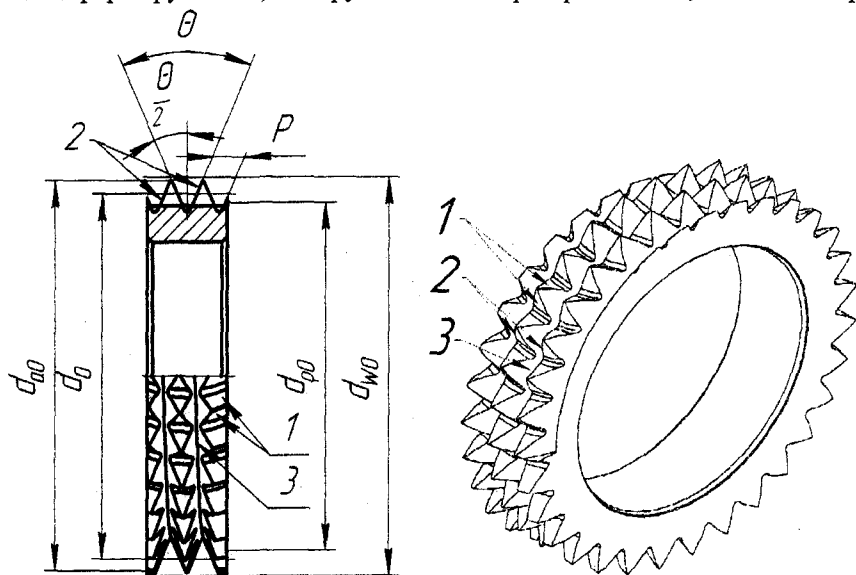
Шевер-прикатник для чистовой обработки цилиндрических колес с круговыми зубьями
